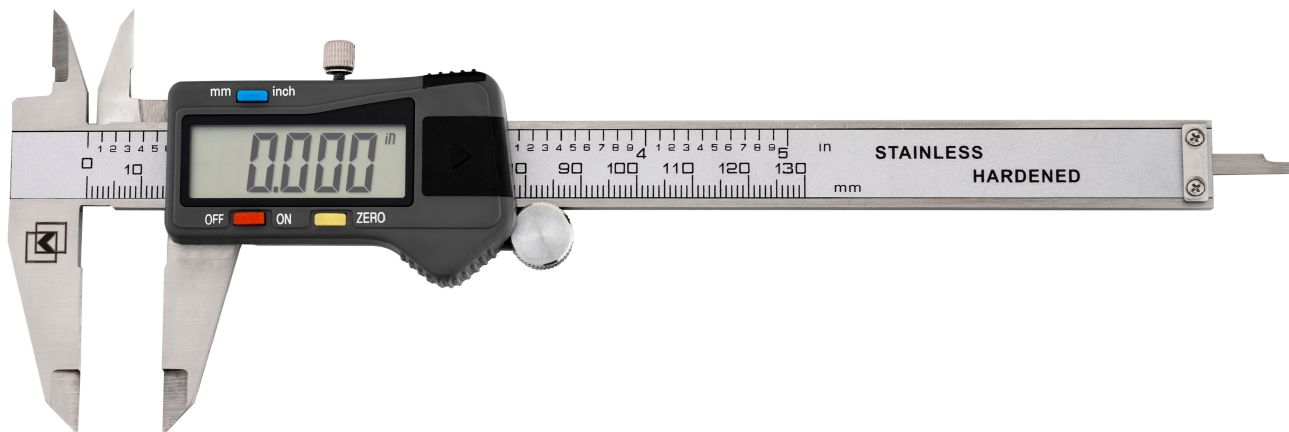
Общий вид штангенциркулей ШЦЦ-I
